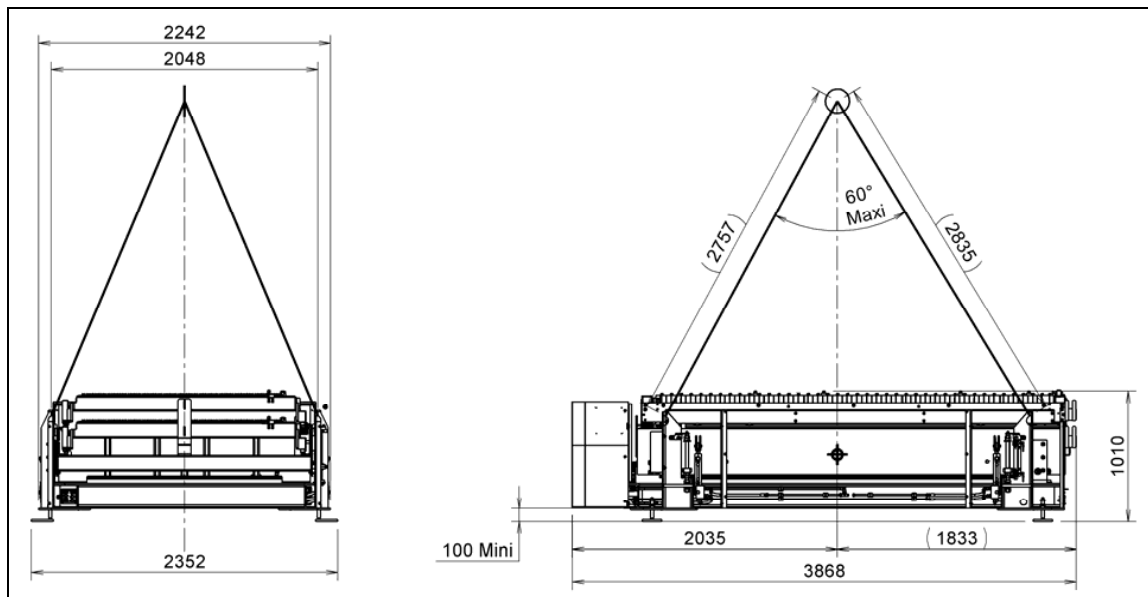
Heben des Palettenwechslers mit einem Kran (Alle Angaben in mm)
